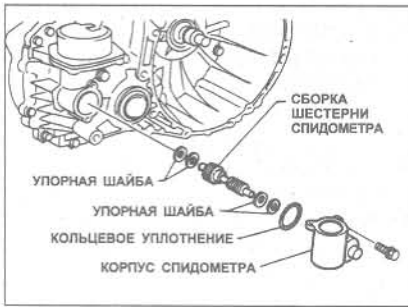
Сборка корпуса спидометра и привода (Глава 12)
